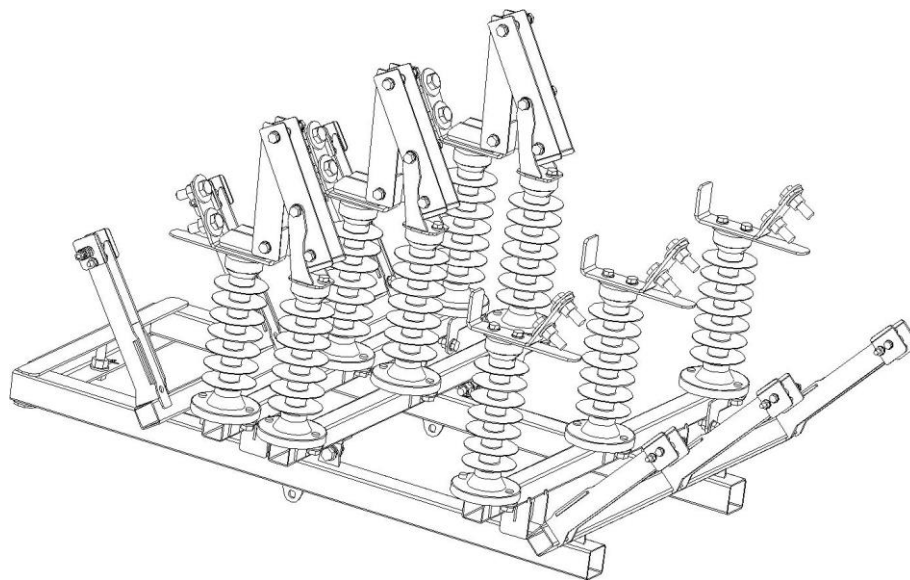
б Конструкция разъединителя с заземлителем с двух сторон
